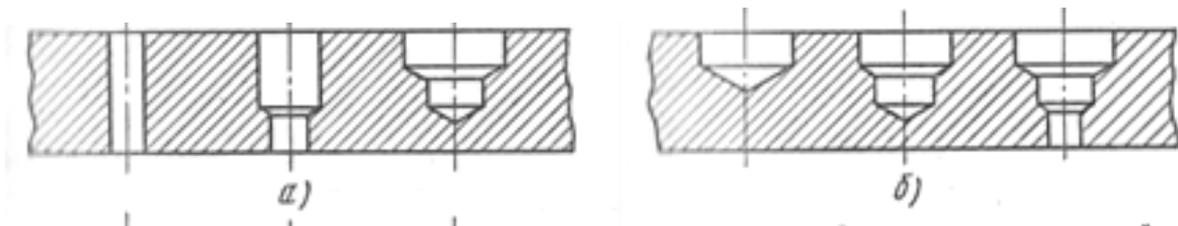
сверление отверстий с уступами: а- рассверливанием, б – с уменьшением диаметра отверстий.
